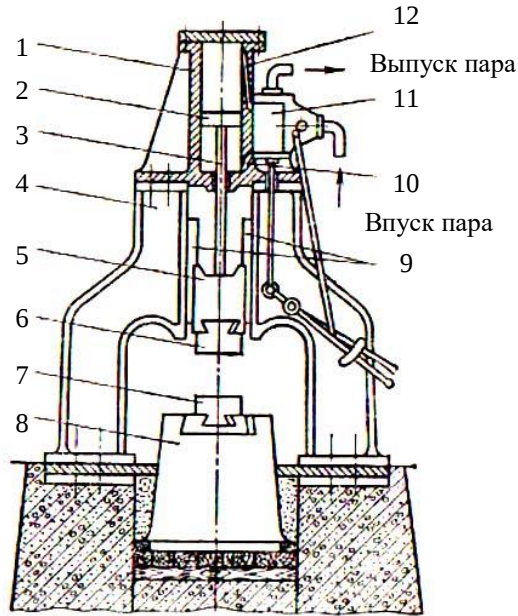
Схема паровоздушного молота арочного типа: 1- рабочий цилиндр; 2- поршень; 3- шток; 4- станина; 5- баба; 6, 7- байки; 8- шабот; 9- направляющие; 10, 11, 12 – газораспределительные устройства
